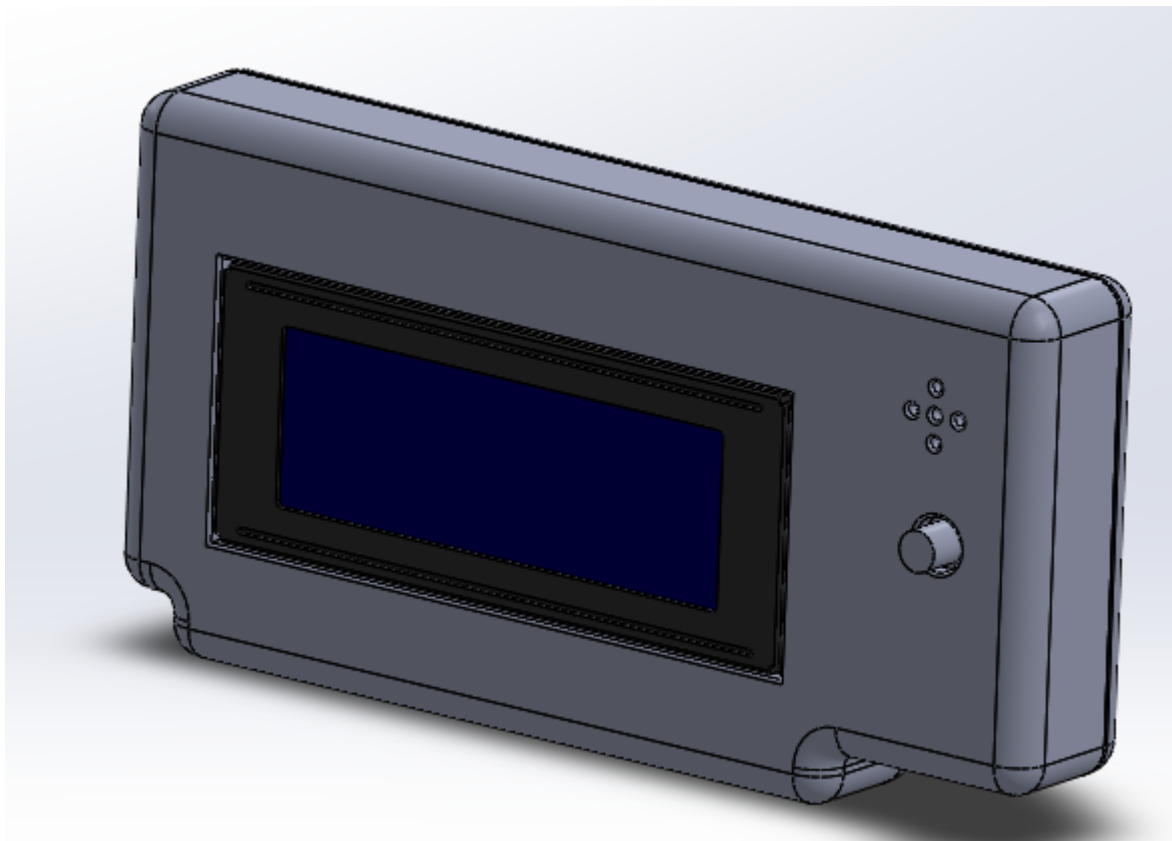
3D модель зібраного корпусу з встановленою електронікою
